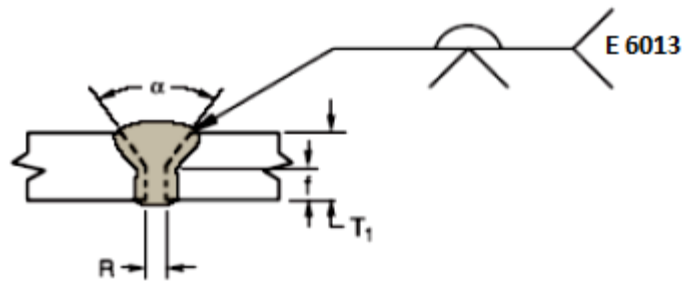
Soldadura de ranura de bisel en V [4].
